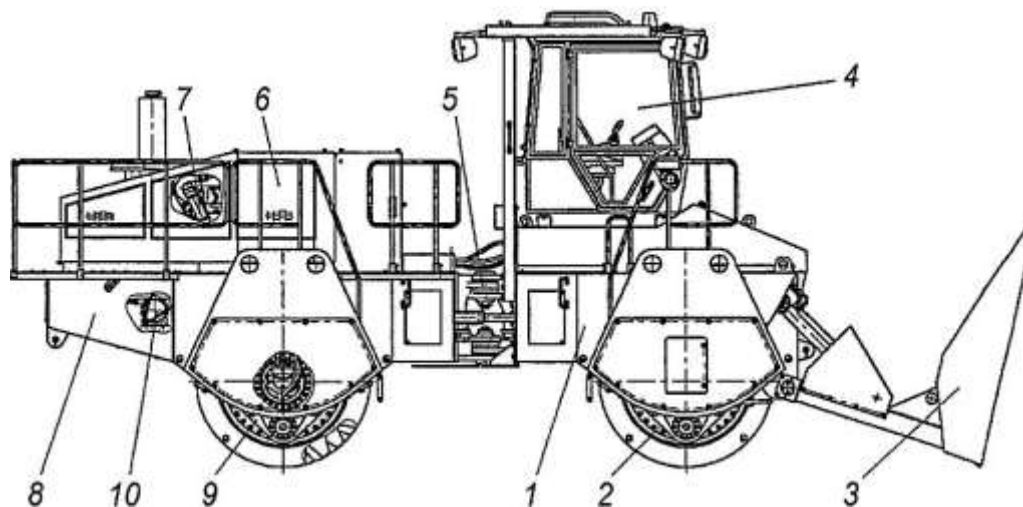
Общий вид уплотнителя РЭМ-25: 1 – рама переднего вальца с топливным баком; 2 – передний кулачковый валец; 3 – отвал; 4 – кабина оператора; 5 – шарнир сочленения; 6 – капот; 7 – силовой агрегат; 8 – рама заднего вальца; 9 – задний кулачковый валец; 10 – подогреватель двигателя
